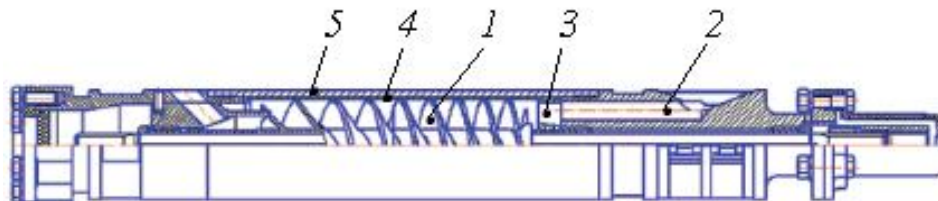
Газосепаратор центробежный (типовая конструкция)
